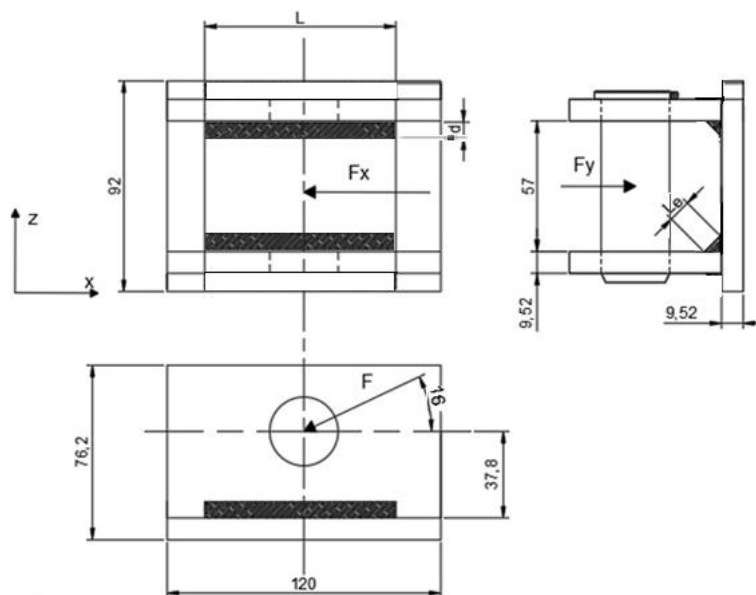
Dimensionamiento cordón de soldadura
